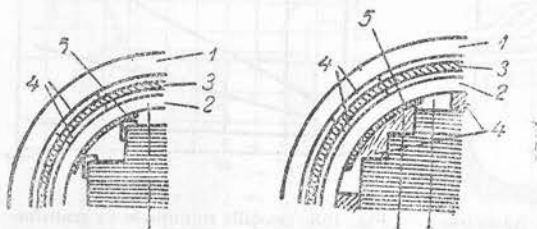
Dispoziție de izolare la bobinaje concentrice: 1 — bobinaj de înaltă tensiune; 2 — bobinaj de joasă tensiune; 3 — tub izolant; 4 — piesă de distanță din pertinax sau preșpan; 5 — preșpan.
